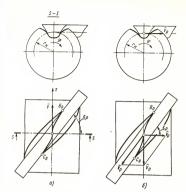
Схема сопряження внитовой поверхности детали с инструментальной рейкой
